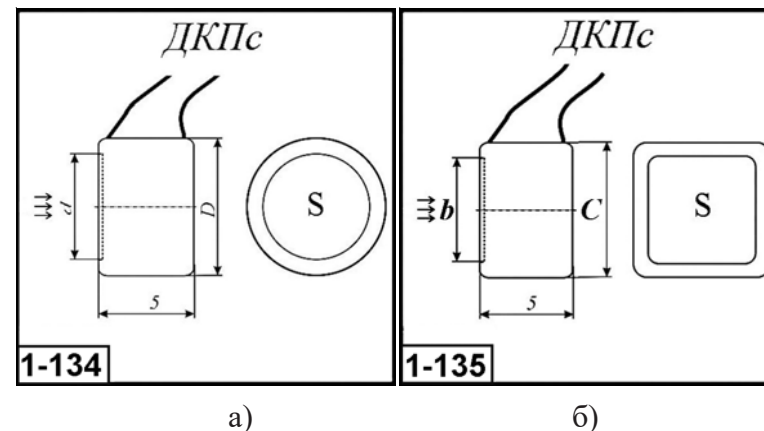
Внешний вид и габаритные размеры детекторов типа ДКПс: а - круглого, б - квадратного.
